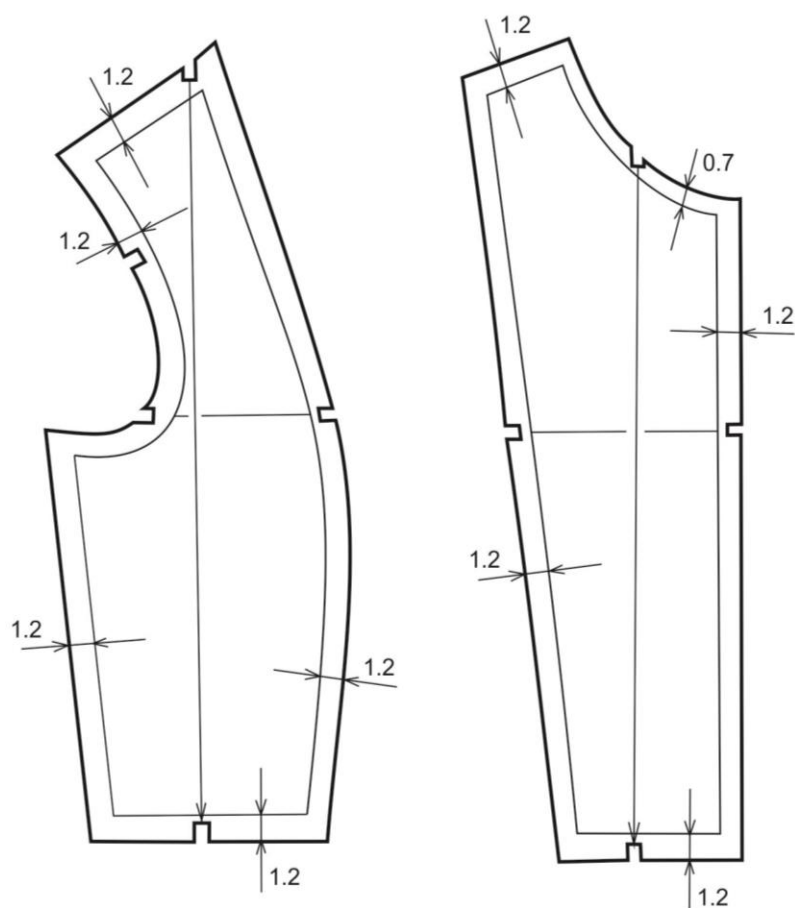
Построение чертежей основных шаблонов деталей верха
